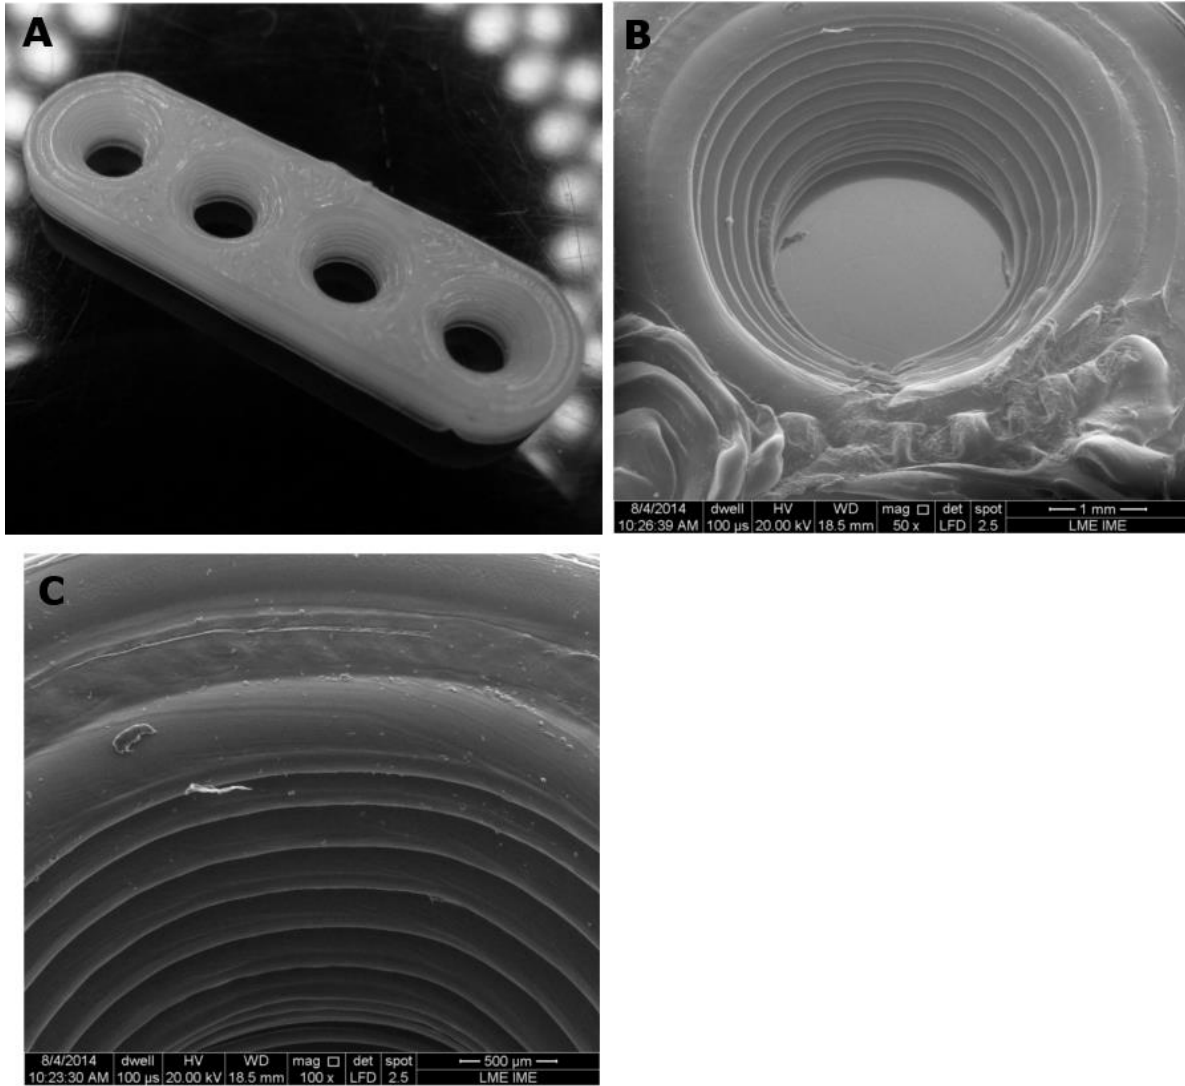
Placa impressa contendo cavidades para passagem dos parafusos de fixação e o efeito em degrau causado pela deposição de camadas.
